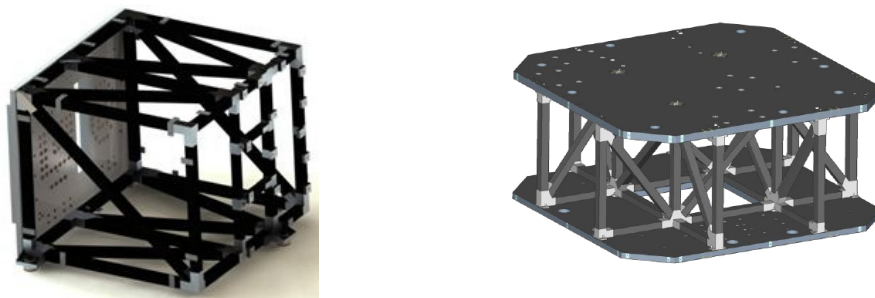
Терморазмеростабильные конструкции платформ ферменного типа с углепластиковыми плитами
